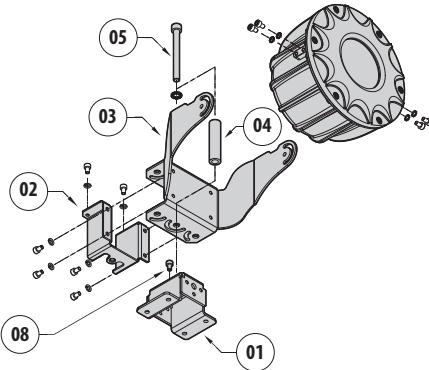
Fissaggio a parapetto con ingresso cavi verso l'alto.
